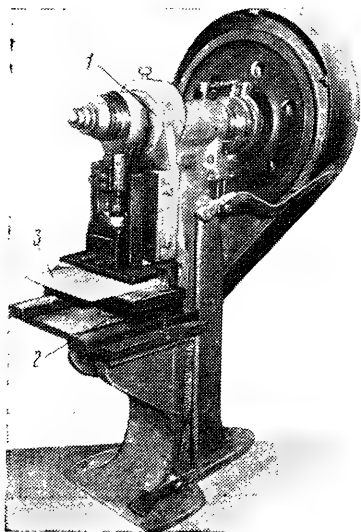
Эксцентриковый пресс для штамповки асбоцементных перегородок:
